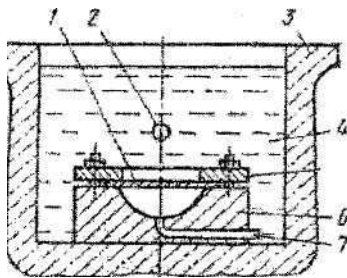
Схема штамповки взрывом деталей из плоской заготовки:
